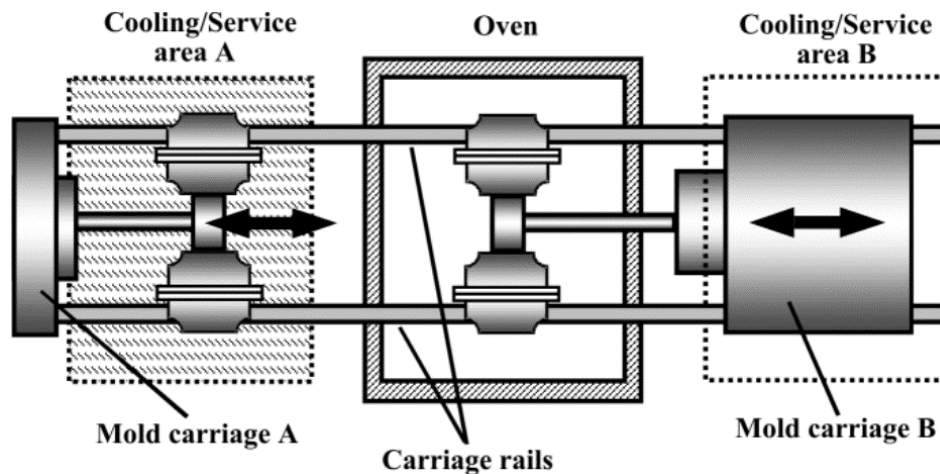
Machine de roto-moulage de type navette, montrant l'ensemble de moules B dans le four et l'ensemble de moules A dans la zone de refroidissement et de service
